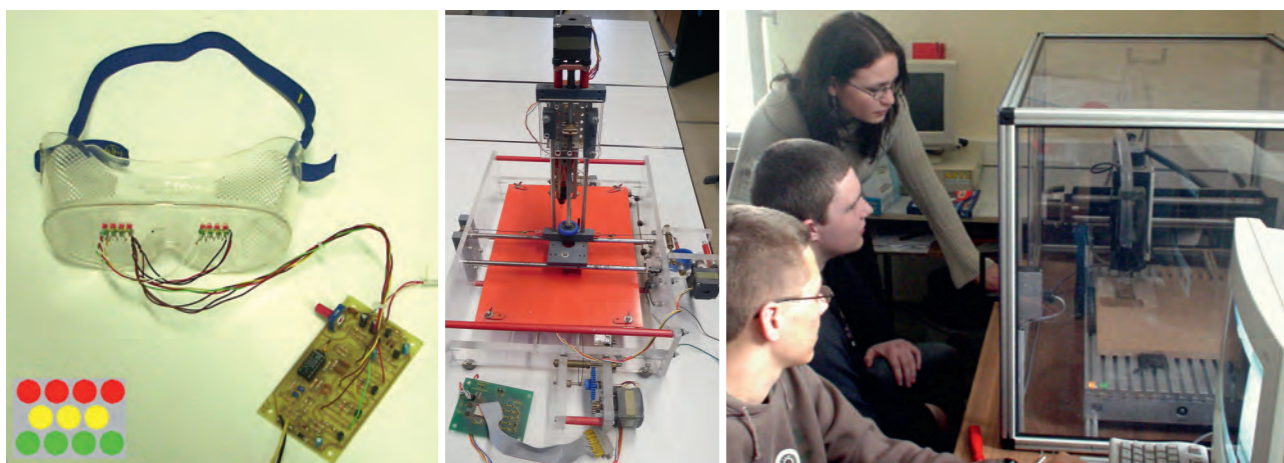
Lichtorgelbrille (links), CNC-Bohrmaschine, Eigenbau (Mitte), Professionelle CNC-Fräsmaschine (rechts)
